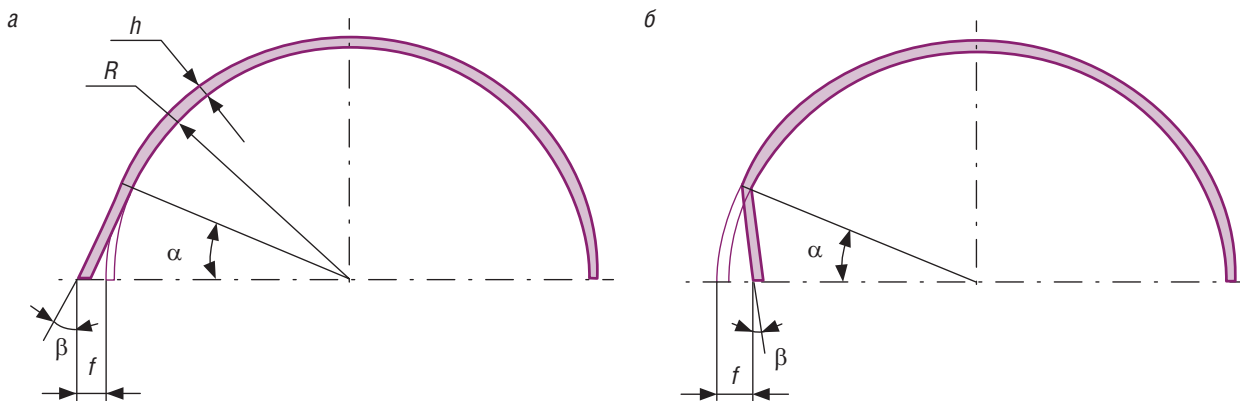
Поперечное сечение котла с уводом кромок сварного шва наружу обечайки (а); с уводом кромок сварного шва внутрь обечайки (б)
